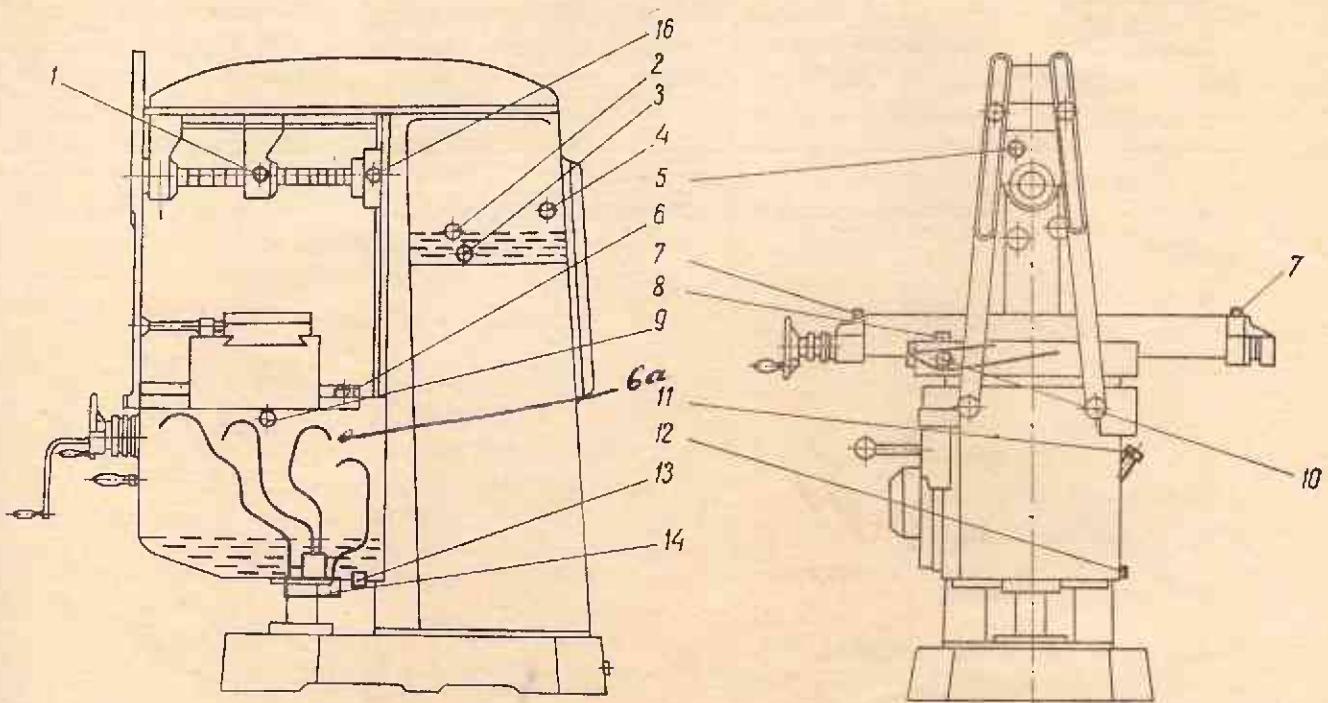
Схема смазки станков 6Н80 и 6Н80Г
